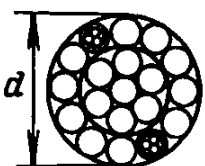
Схема круглой токопроводящей жилы силового кабеля с двумя контрольными жилами
